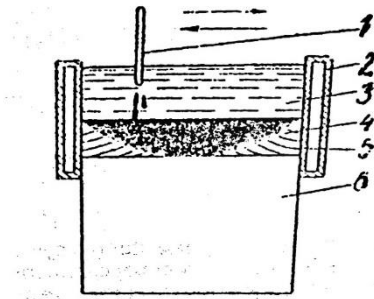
ЕШН плоскої поверхні електродним дротом у горизонтальному положенні: 1 – електрод; 2 – кристалізатор; 3 – шлакова ванна; 4 – металева ванна; 5 – наплавлений шар; 6 – заготівля
